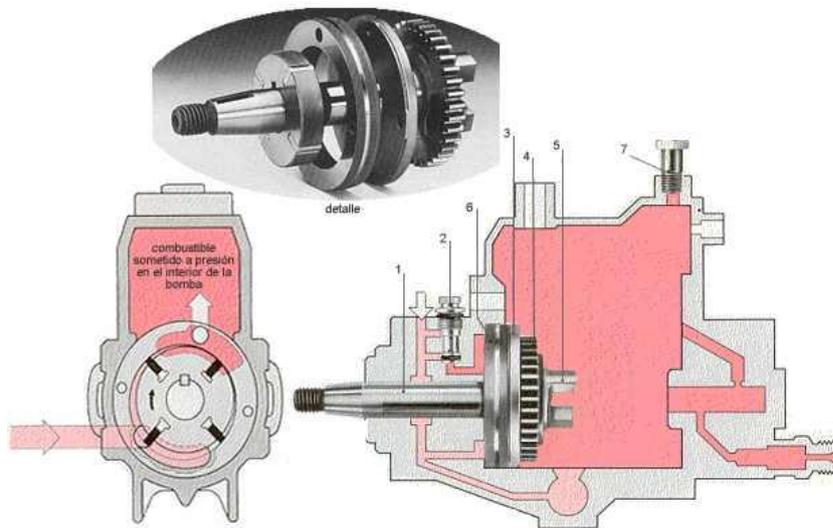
Despiece de baja presión de una bomba de inyección
